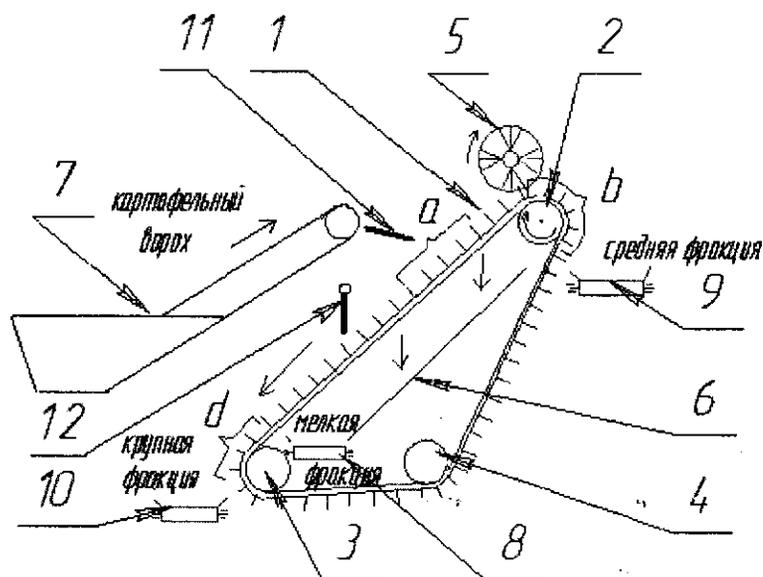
Устройство для разделения картофельного вороха на фракции: 1 – калибрующее полотно; 2 – ведущий вал со шкивами; 3, 4 – направляющие и обводные шкивы; 5 – сталкивающий щеточный барабан; 6 – поддерживающая горка; 7 – загрузочный бункер с подающим транспортёром; 8, 9, 10 – транспортёры крупной, мелкой, средней фракций; 11 – направляющий лоток; 12 – гаситель скорости клубней.
